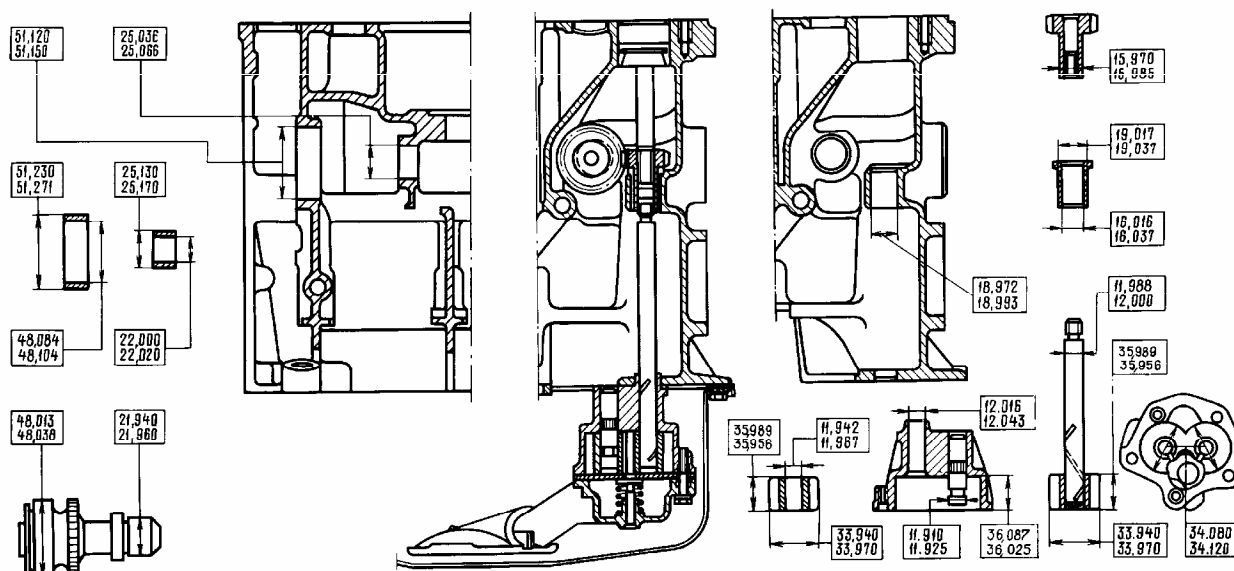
Основные размеры деталей масляного насоса и его привода
